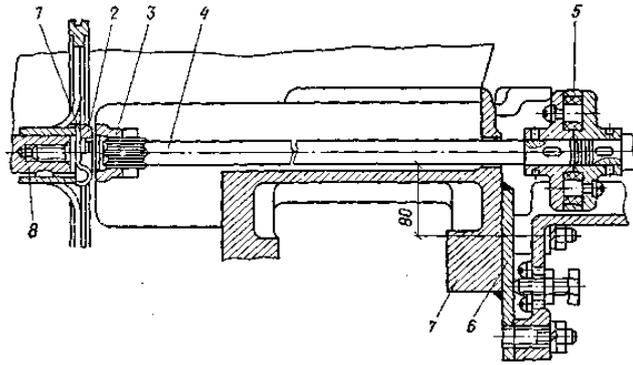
Установка насоса НШН-600 на тракторы Т-40, Т-40А: 1 – замковая шайба; 2 – контргайка; 3 – храповик; 4 – приводной вал; 5 – муфта; 6 – косынка; 7 – передний брус рамы; 8 – коленчатый вал двигателя
